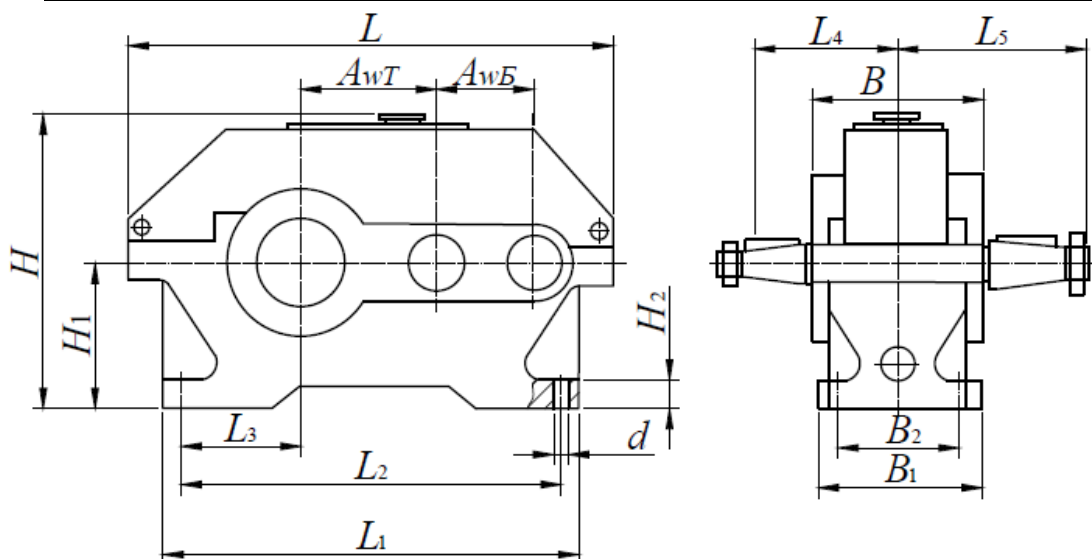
Редукторы цилиндрические двухступенчатые типа Ц2У
